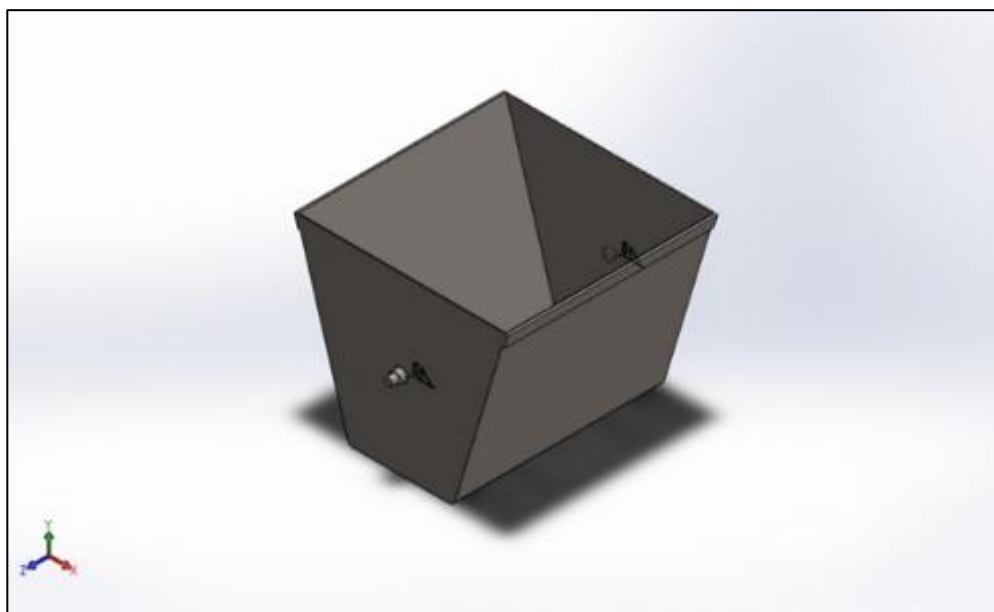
Modelado de la cubeta para elevar el concreto mezclado.
